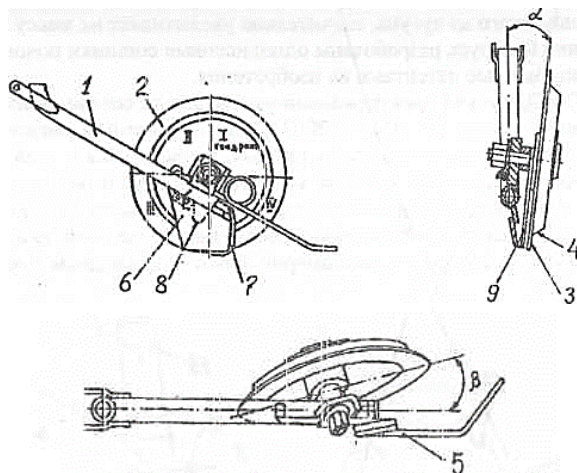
Однодисковый сошник тарельчатой формы: 1 – крепежная труба; 2 – тарельчатый диск; 3 – плоская поверхность диска; 4 – опорная поверхность диска; 5 – загорточ; 6 – киль; 7 – клапан; 8 – выходное отверстие семянаправителя; 9 – направляющая пластина
